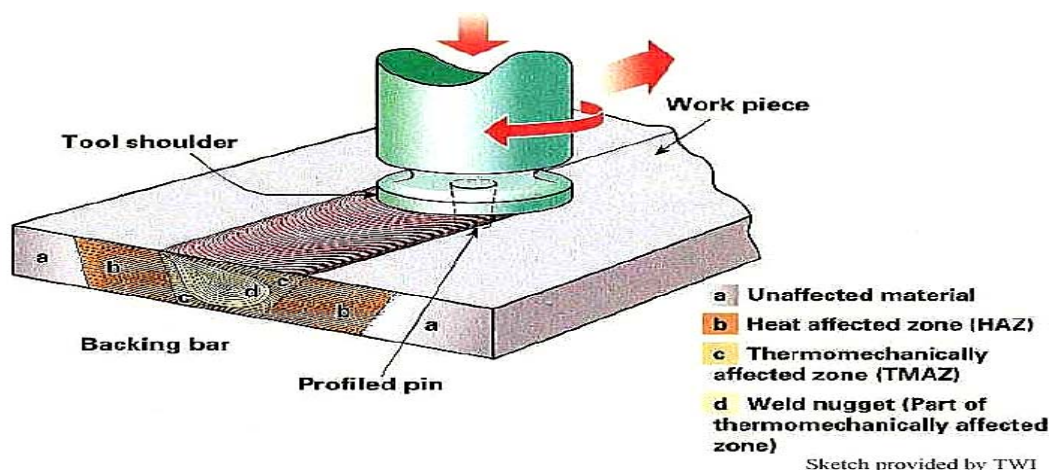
Montagem de FSW - Friction Stir Welding (SFL). [62]
